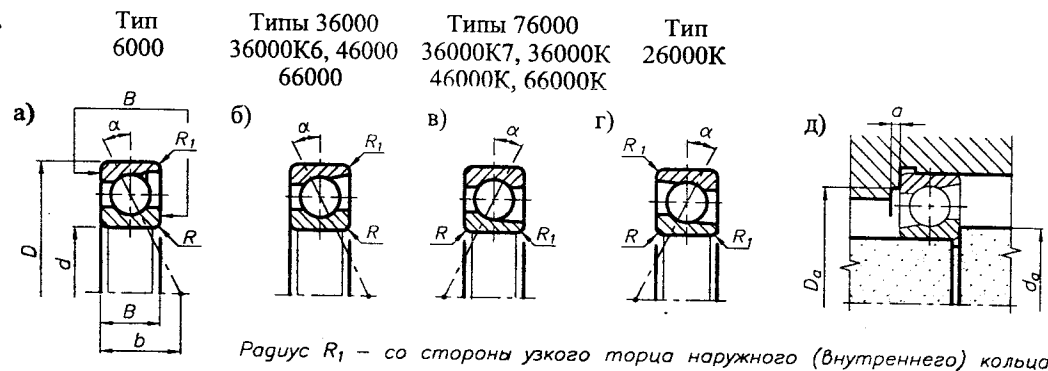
Габаритные и установочные размеры шариковых радиально-упорных подшипников
